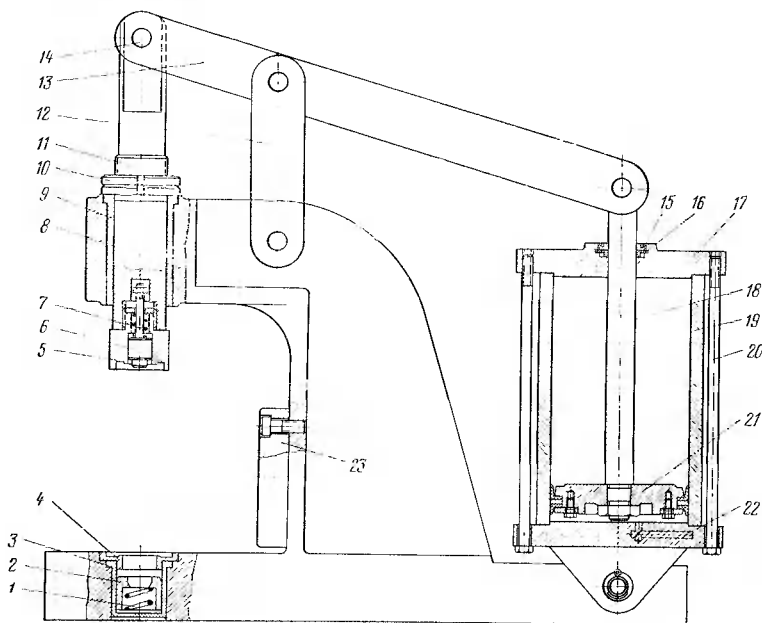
Оправка для установки упорного кольца на задний подшипник коленчатого вала компрессора:
